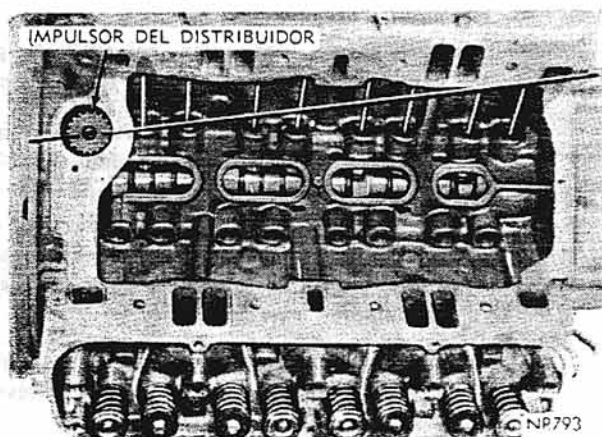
Instalación del Engranaje Impulsor del Distribuidor
